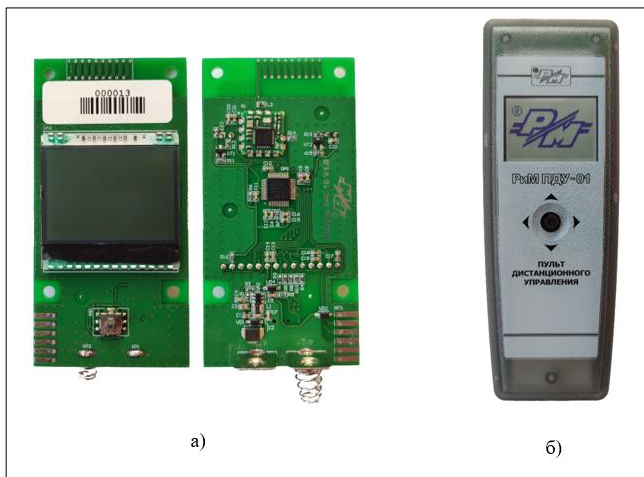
а) внешний вид печатной платы устройства; б) внешний вид устройства, собранного в корпус
